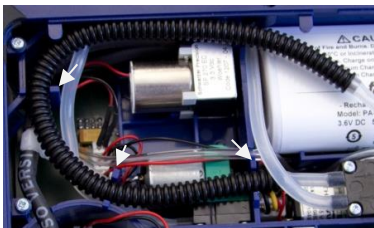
Wellenschlauch korrekt verlegt; Führungshaken mit Pfeil markiert
